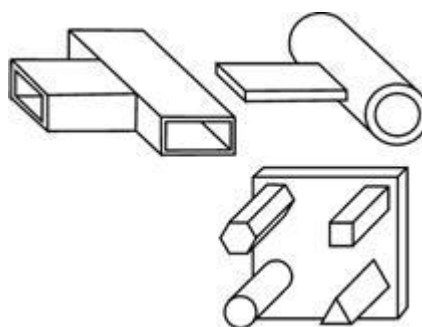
Типы сварных соединений, которые могут быть выполнены орбитальной и линейной сварками трением.
